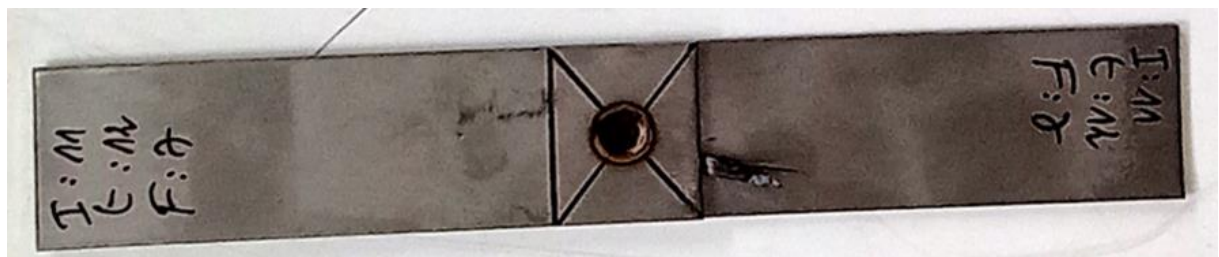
Exemples de réalisation d'assemblages par soudage par points
